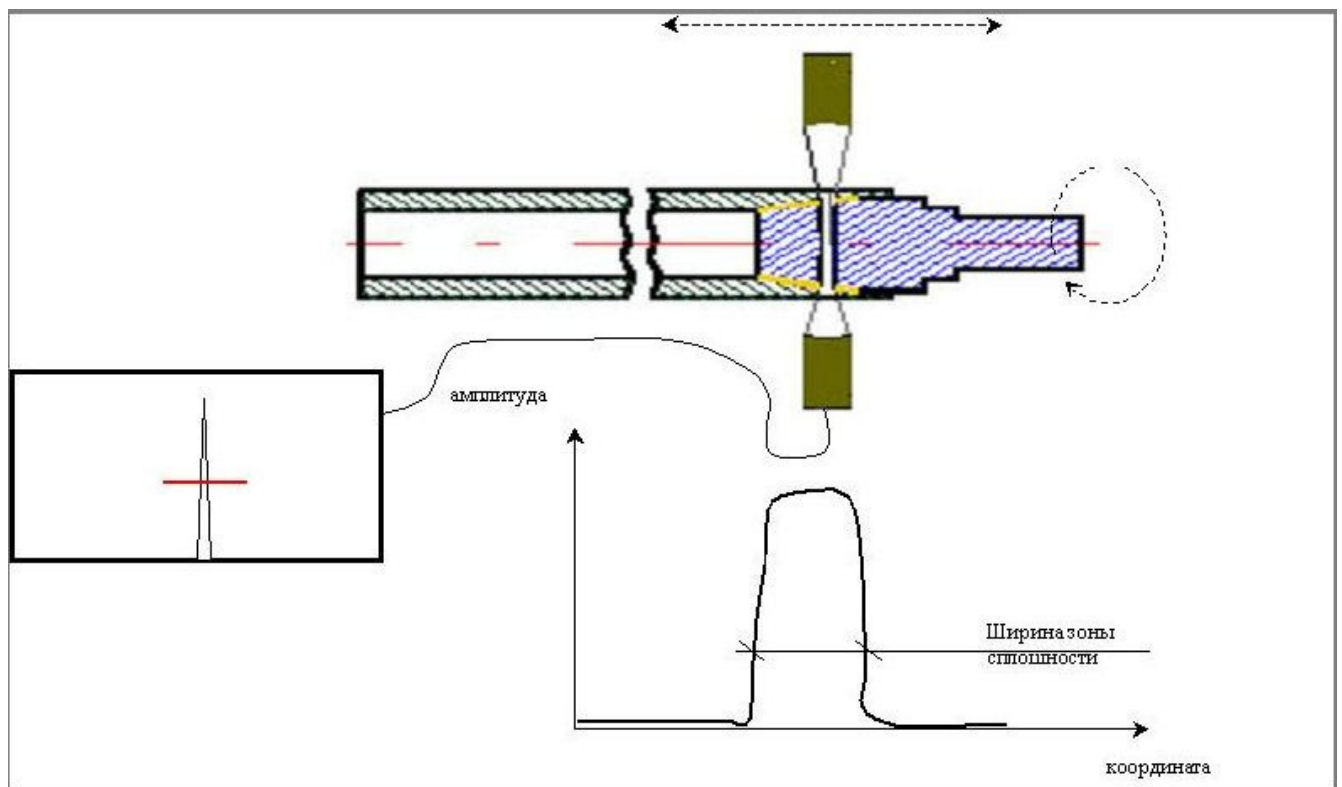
Схема ультразвукового контроля сварного шва КСС твэла ВВЭР-1000
